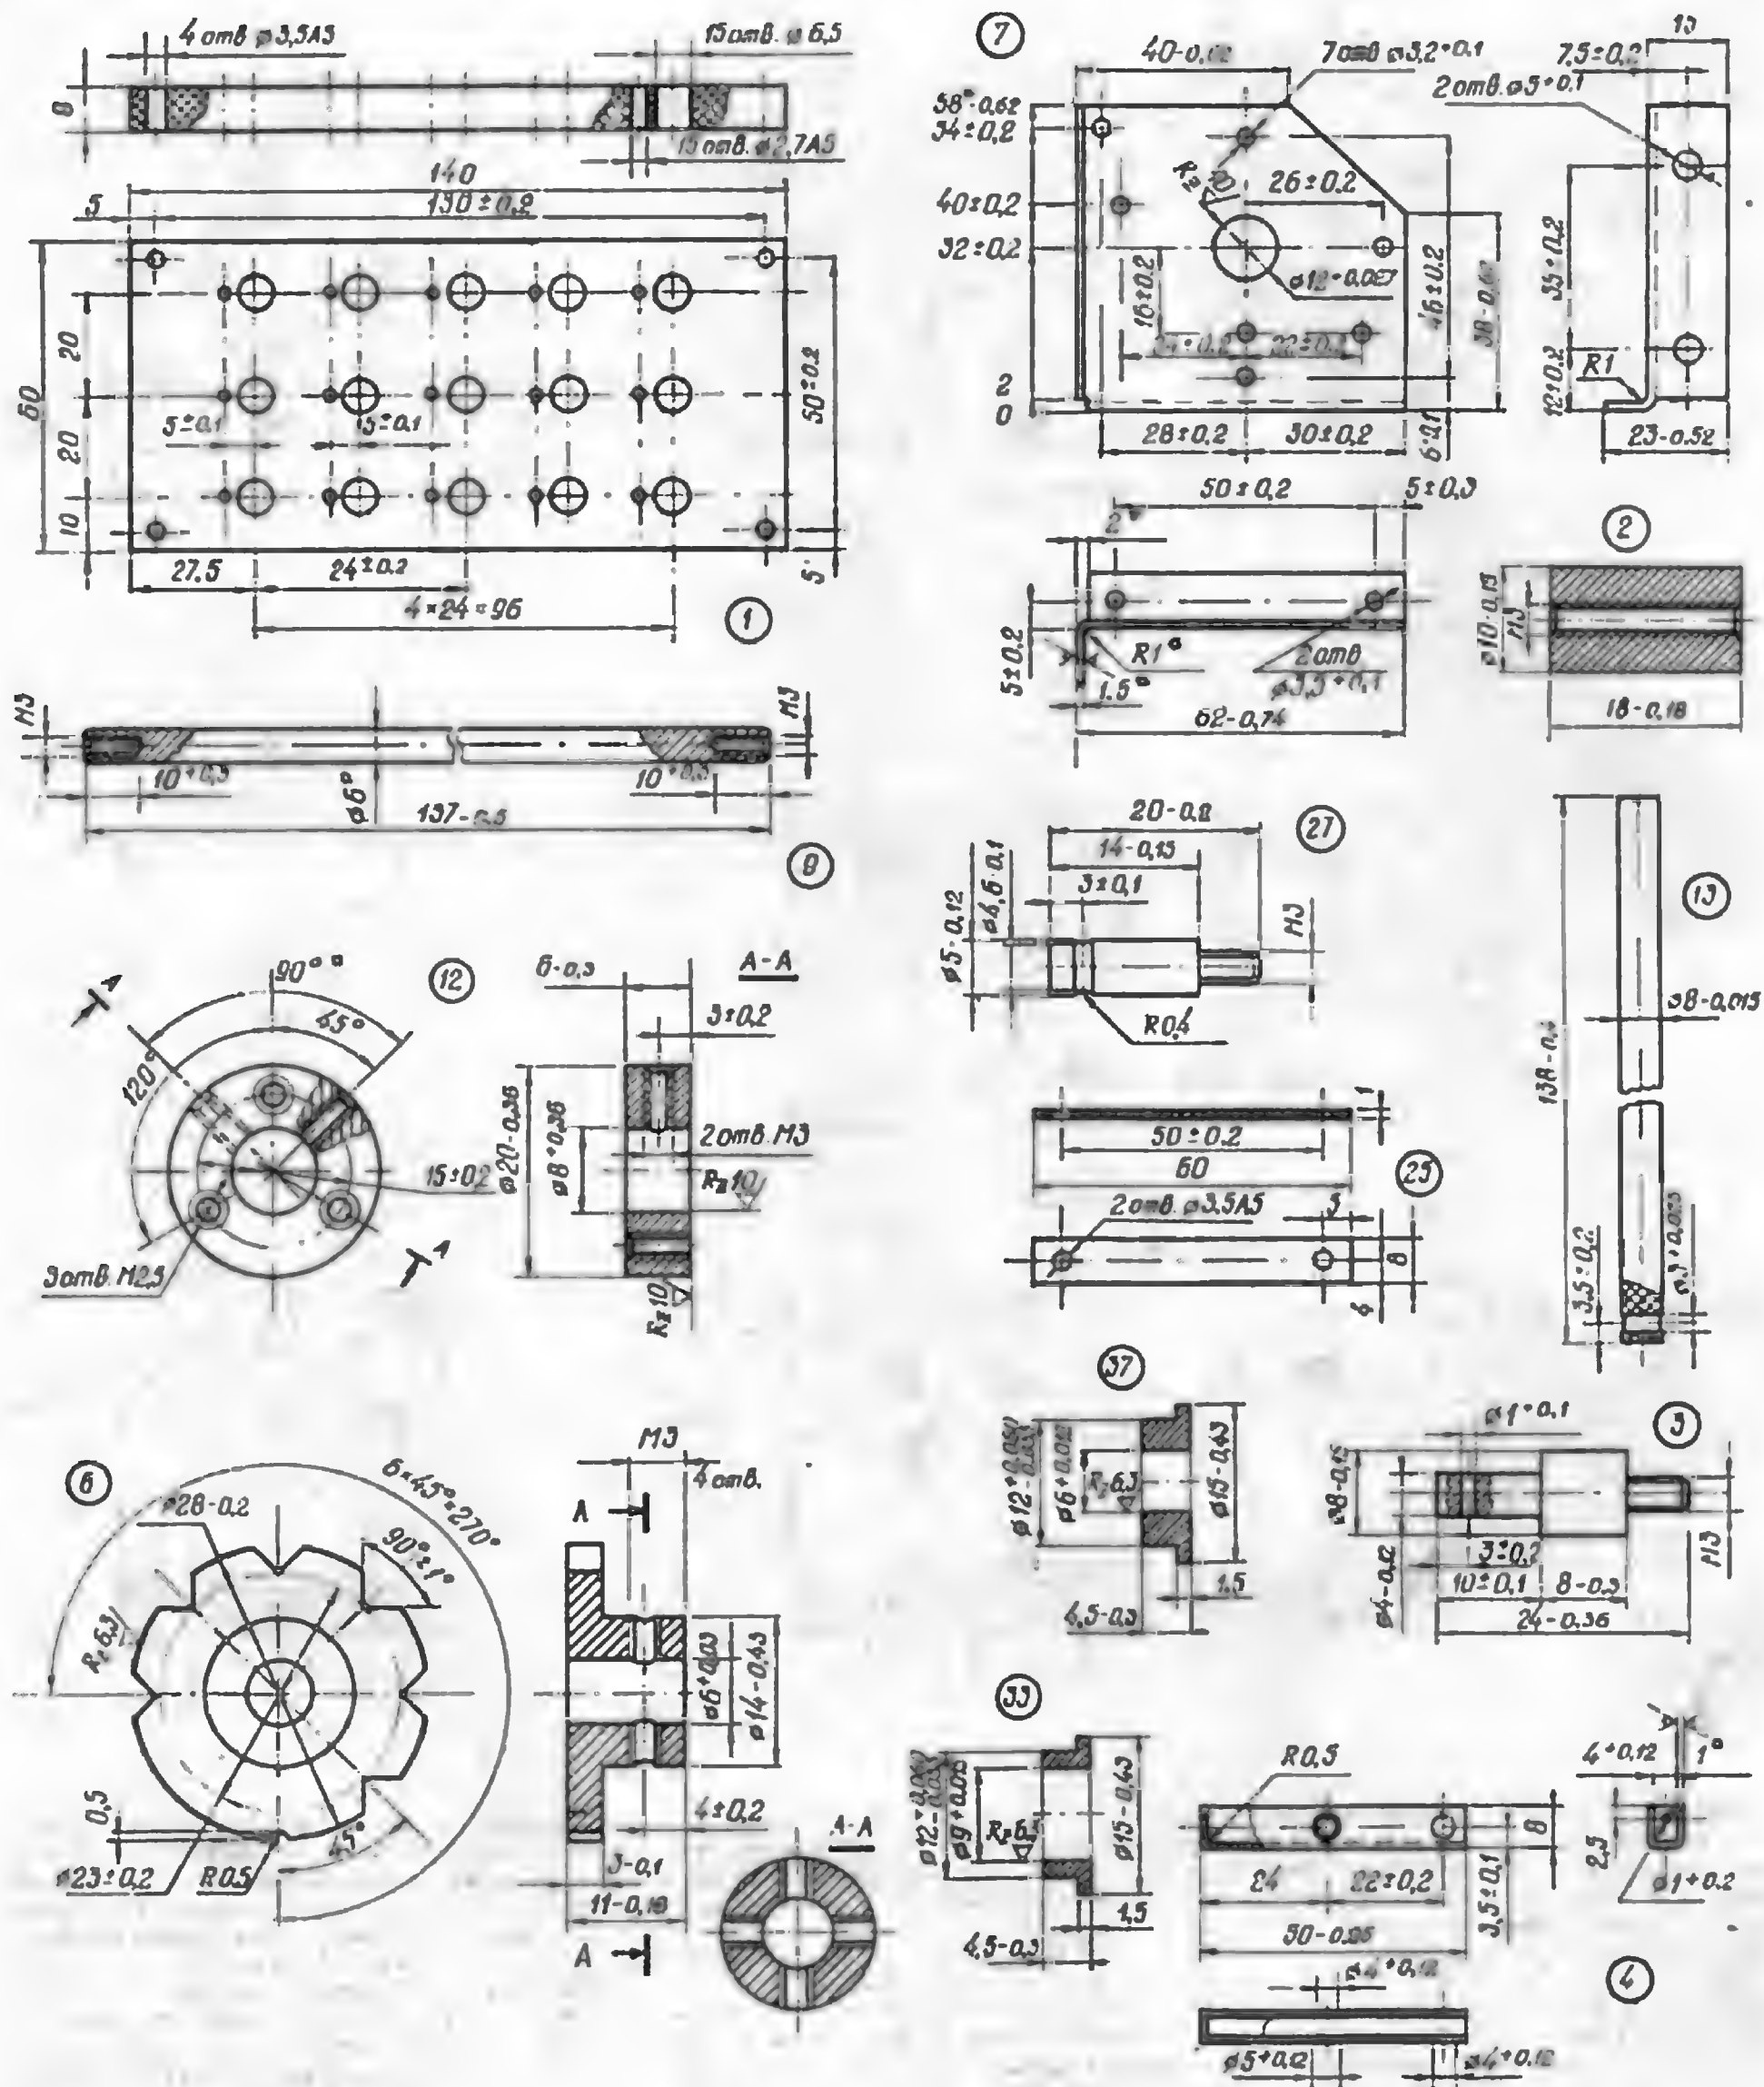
Чертежи деталей переключателя. Размеры, отмеченные звездочкой, даны для справки
